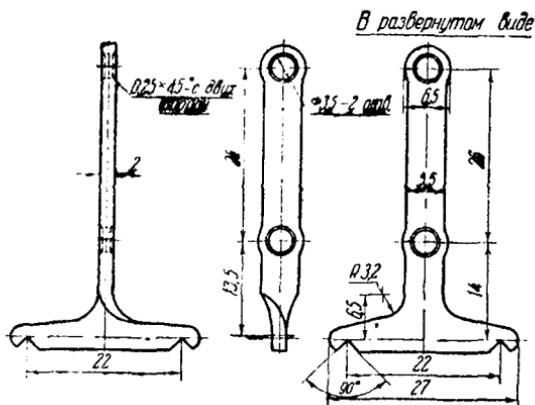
Дет. № 05-226. Коромысло-рычаг стержня поплавка
